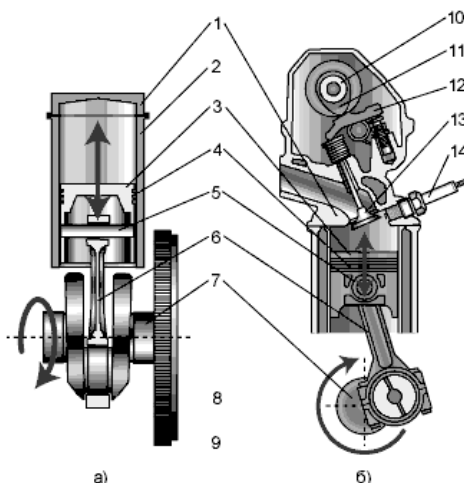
Одноцилиндровый карбюраторный двигатель внутреннего сгорания (а) продольный разрез; б) поперечный разрез):
